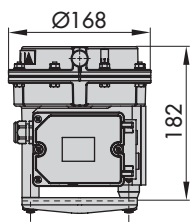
Desenho dimensional da versão de 120 cm²
